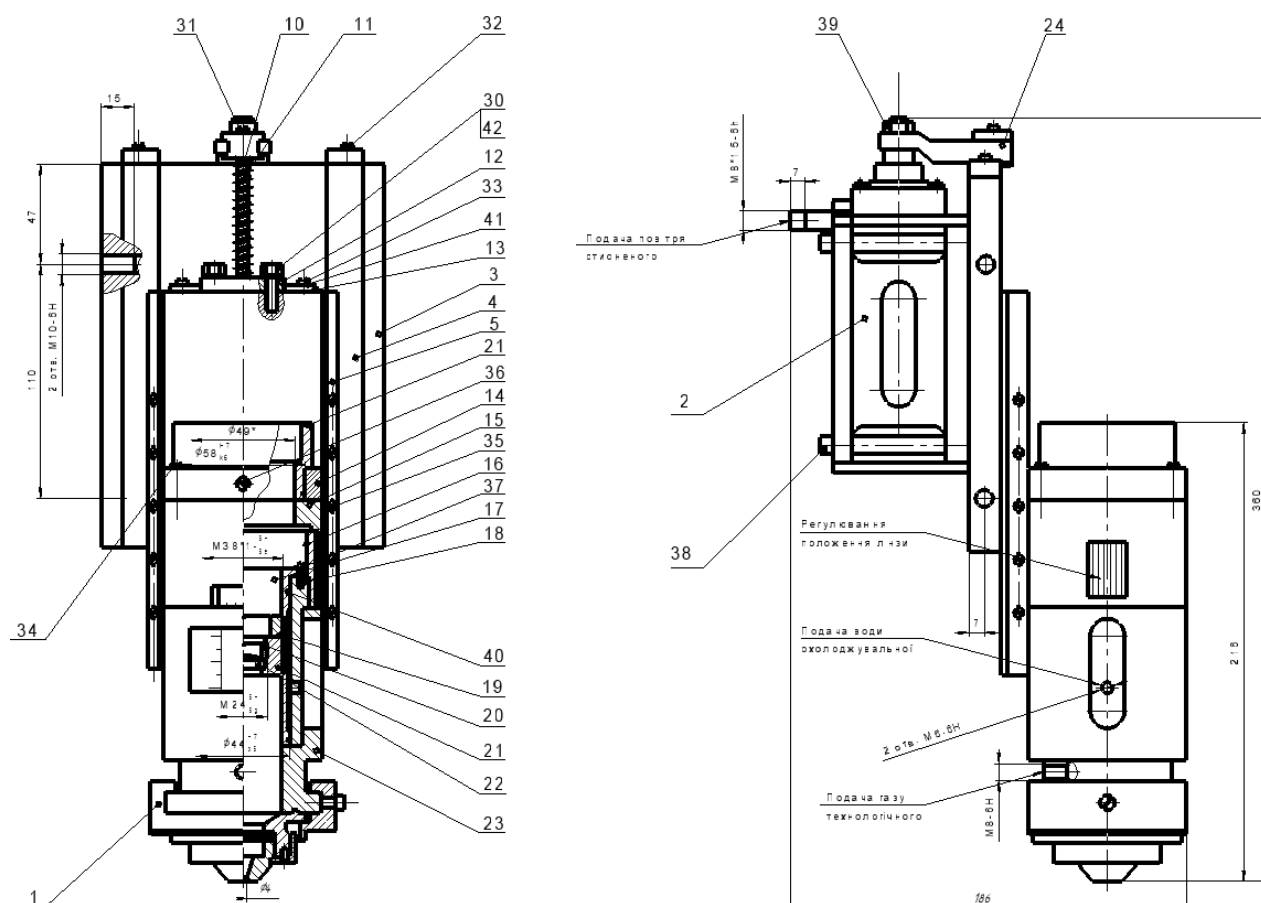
Об'єктив – оптична система для концентрації лазерного проміння: 1 – Блок сопловий; 2 – циліндр пневматичний; 3 – корпус; 4 – направляючі; 5 – салазки;
